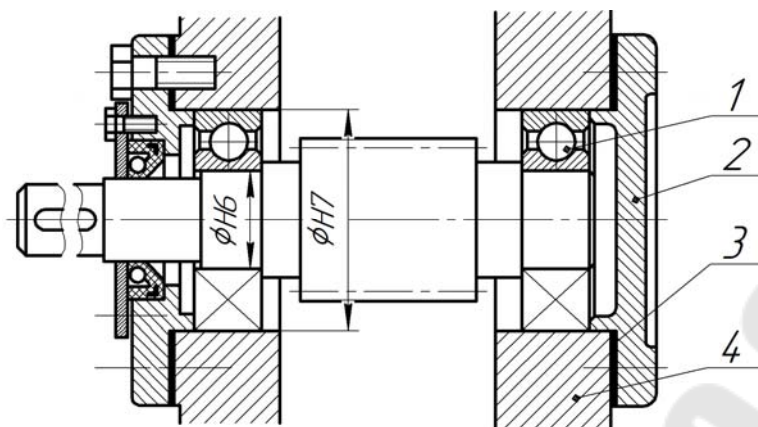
Подшипниковый узел с радиальными подшипниками, установленными «враспор»
